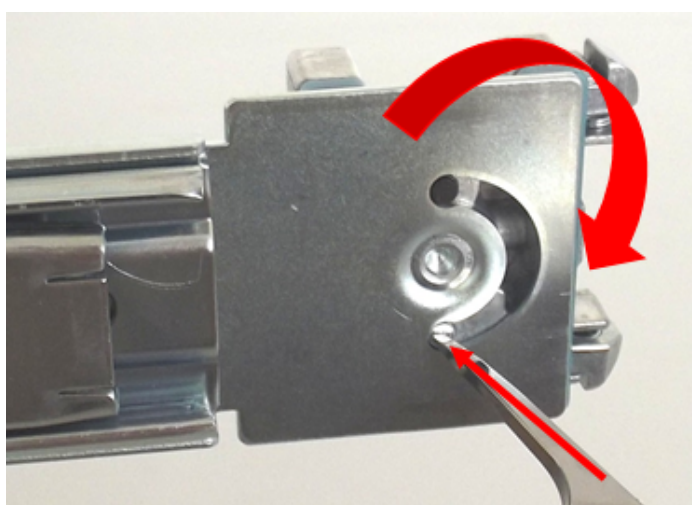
Drücken des Bolzens auf der Innenseite der Halterung
